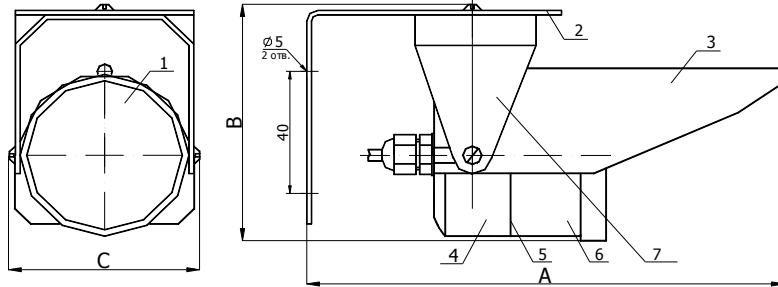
Общий вид извещателя ИД-40, ИД-50
